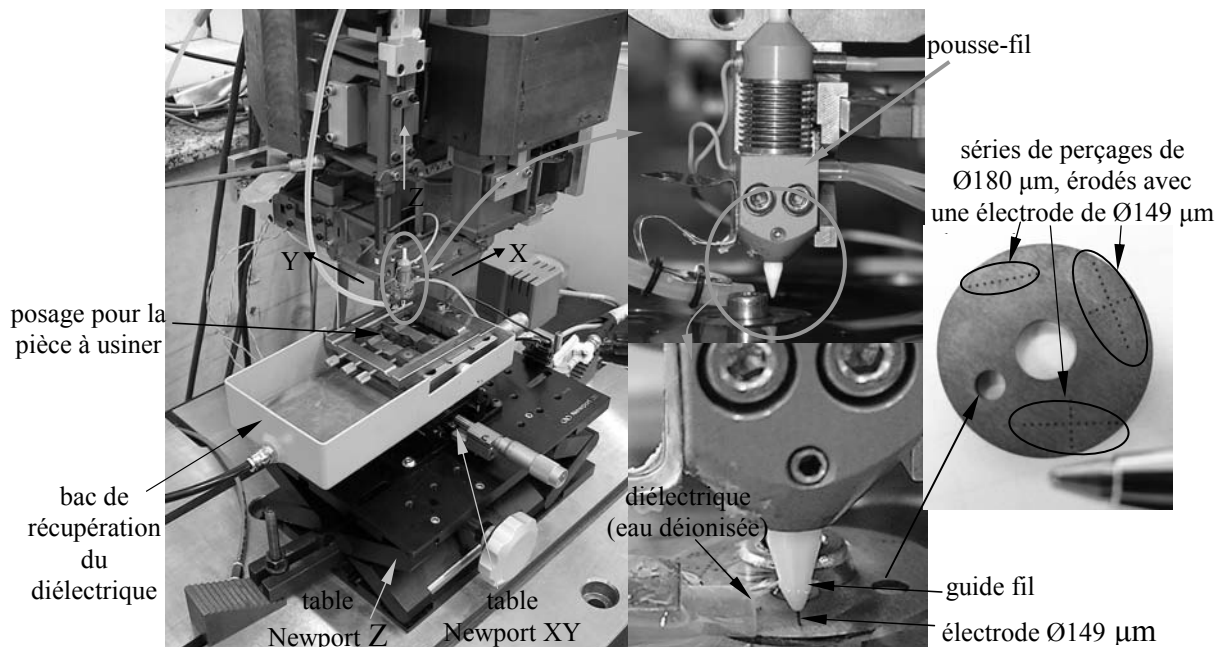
Prototype de machine μ EDM (le Delta³)
